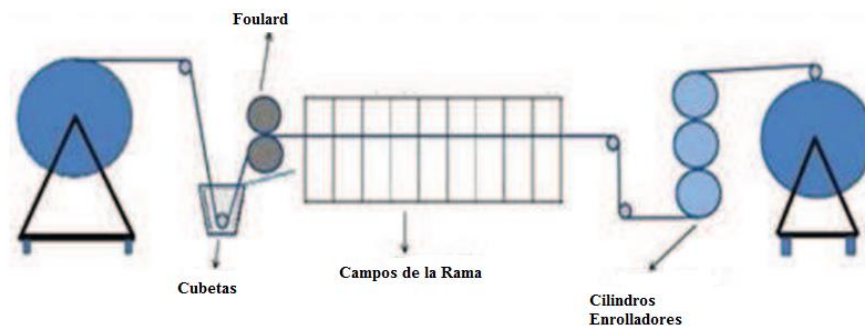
Esquema de aplicación de un apresto antipilling en Rama
